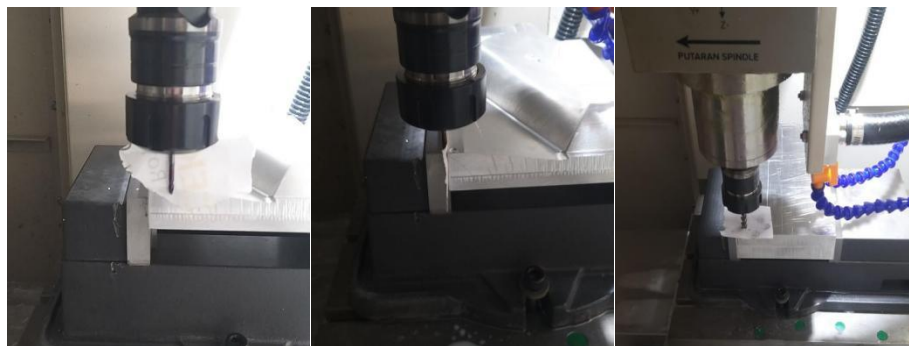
menyalakan mesin Milling Supermill MK 2.0
